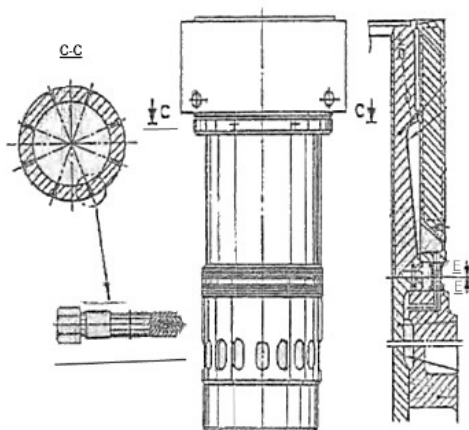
Составная втулка двигателя S70MC В верхней части блока имеются лючки для доступа в отсек распределительного вала. Рамовые подшипники коленчатого вала расположены в поперечных переборках блока, имеют верхний и нижний вкладыши с заливкой белым металлом. Поскольку коленчатый вал подвесной — он заводится снизу и лежит на нижних крышках рамовых подшипников.
